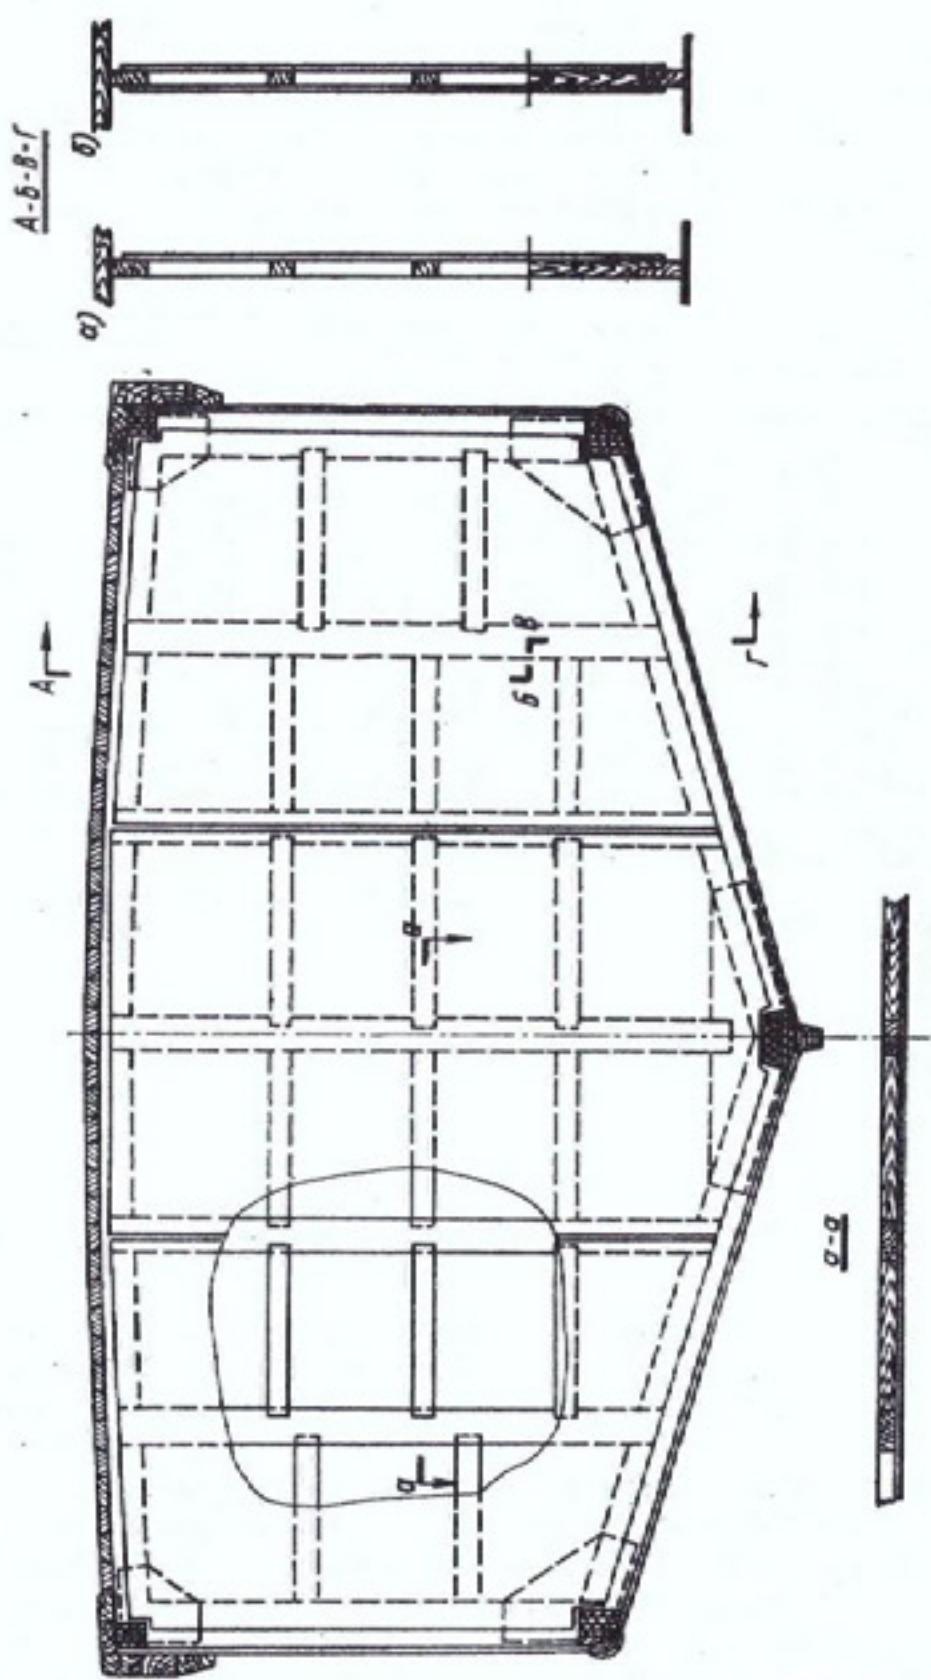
Поперечная переборка с обшивкой из бакелитированной фанеры: а — однослоиняя обшивка; б — двухслойная обшивка.
